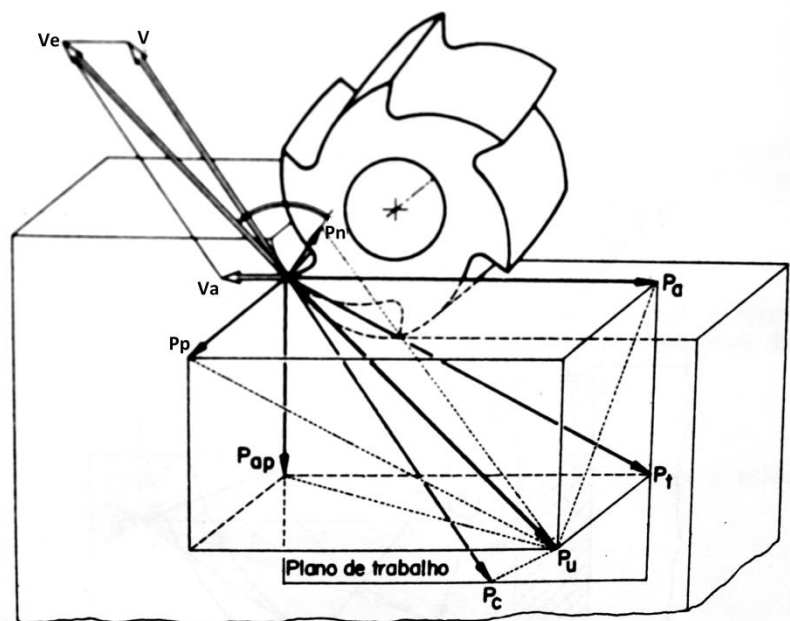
Componentes da força de maquinagem no processo de fresagem (DIN 6584); [Dino Ferraresi, 1970]
